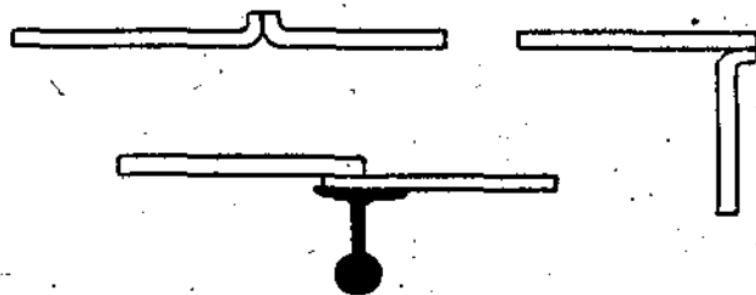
Отбортовка кромок при стыковой сварке.
